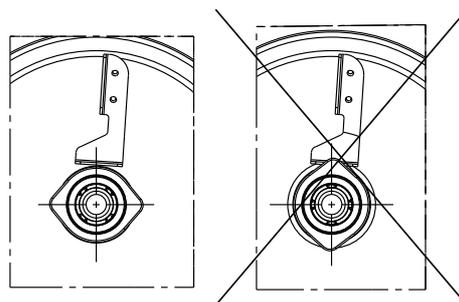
Instalar o O-ring na peça fixa do empanque.
